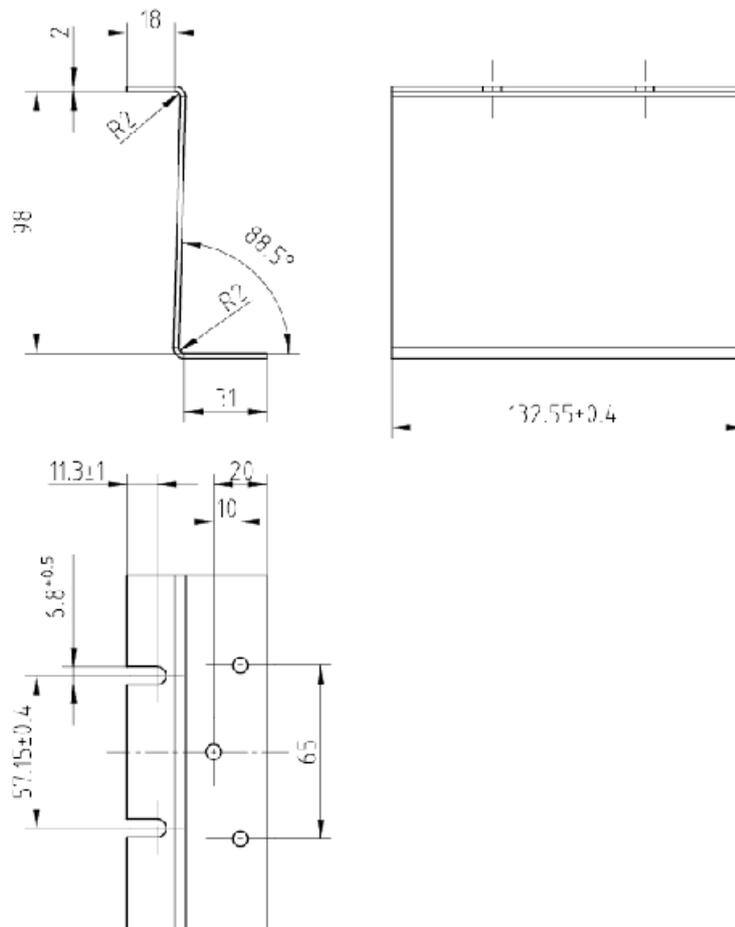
Soporte para montaje de pieza lateral de X-300EEC (medidas en mm)
